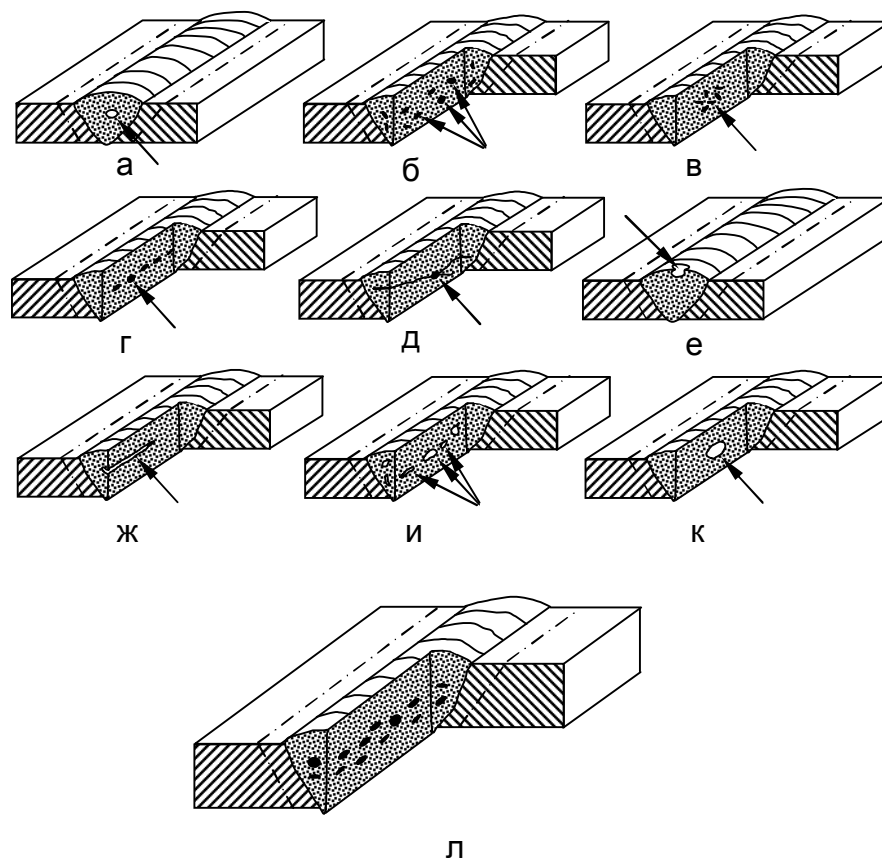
Поры в металле сварного шва: газовая пора (а); распределенная пористость (б); скопление пор (в); цепочка пор (г); пора в сварном ядре (д); поверхностная пора (е); удлиненная раковина (ж); скругленные полости (и); пузырь (к), шлаковые включения в сварном шве (л)
